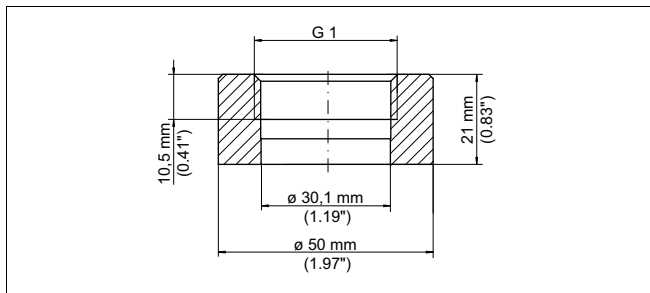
Medidas da luva soldada G1 B conforme ISO 228-1
